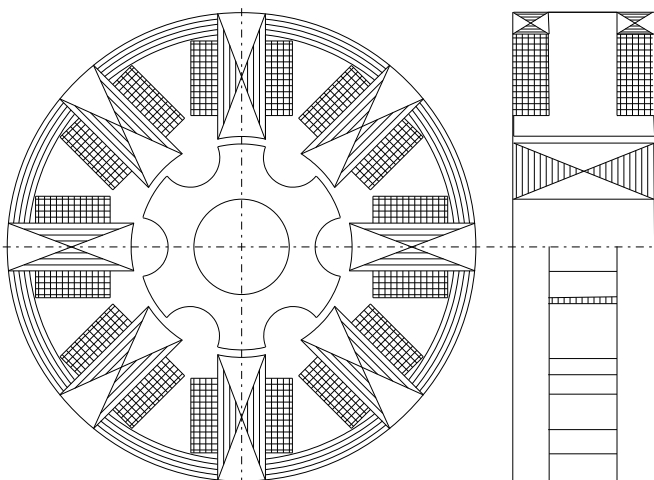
Електромеханічний перетворювач з T-подібними елементами статора
